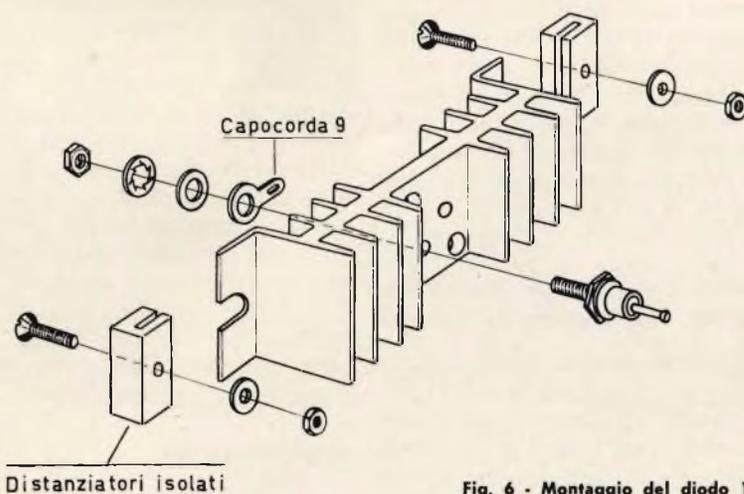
Montaggio del diodo 12 F10 e del dissipatore.
